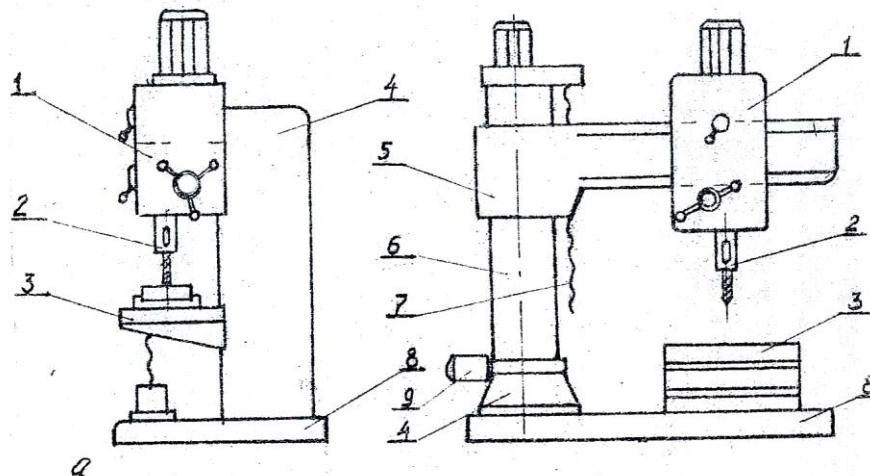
Вертикально-свердлувальний (а) та радіально-свердлувальний верстати (б)
